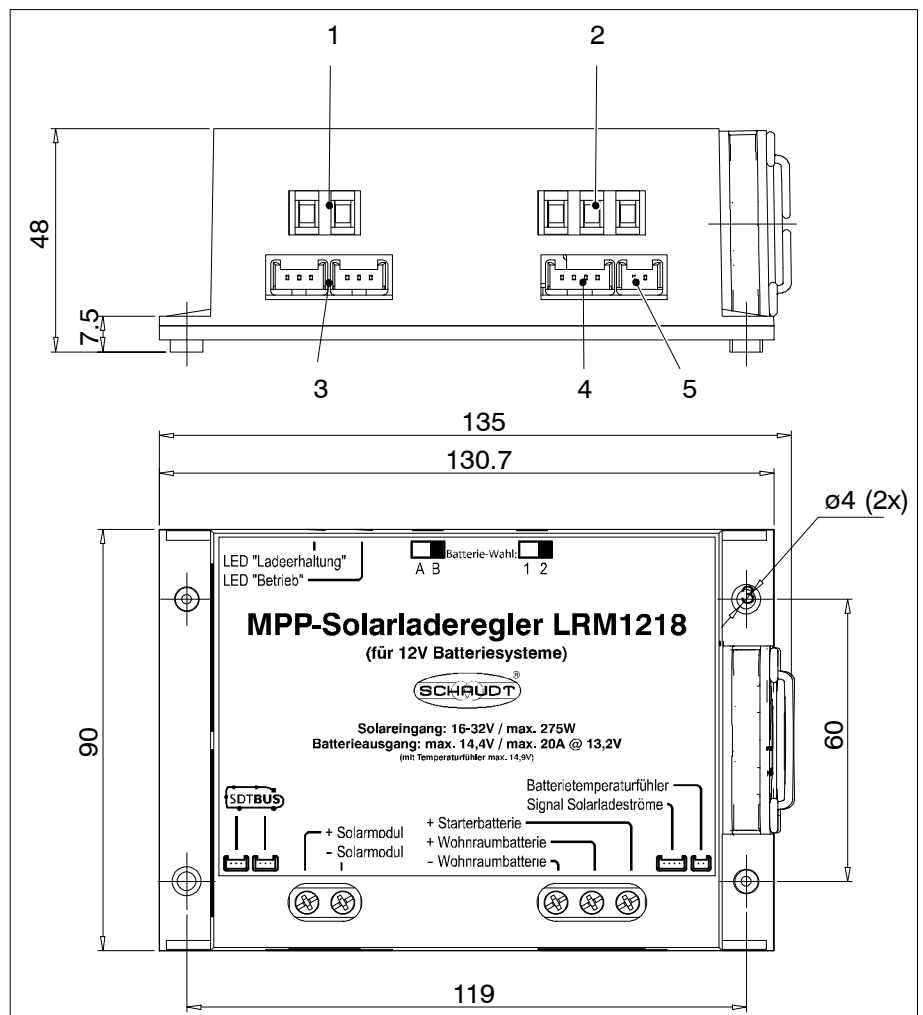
Abmessungen und Anschlüsse Solar-Laderegler LRM 1218
